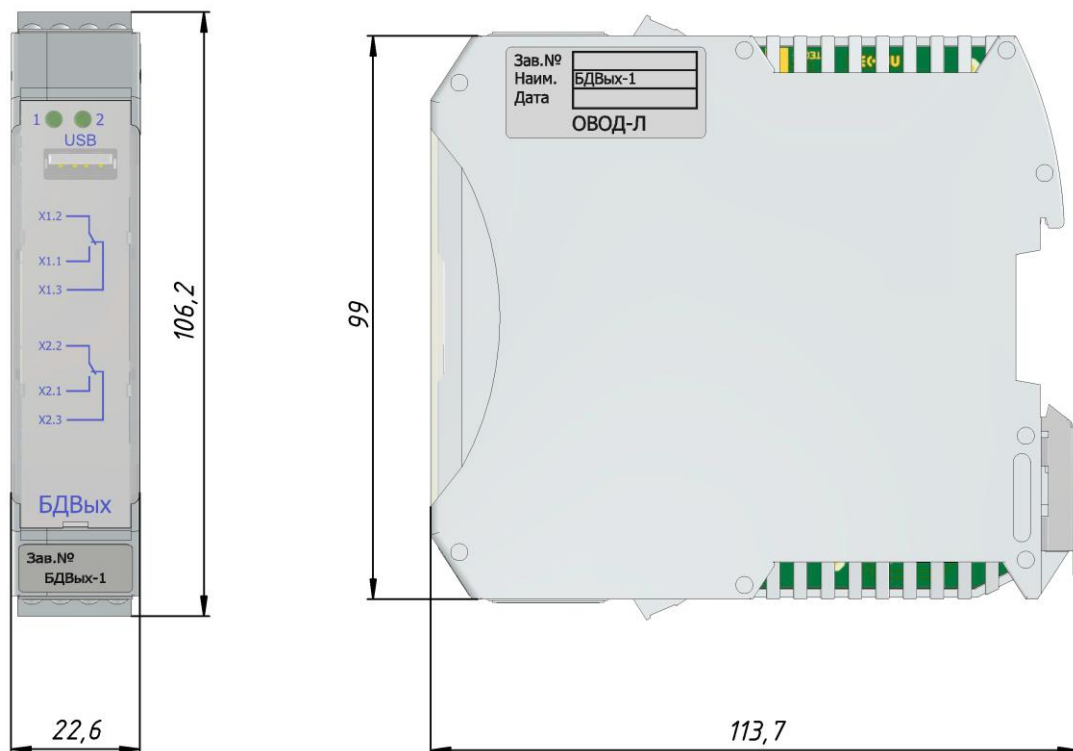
Внешний вид и габаритные размеры БДВых
